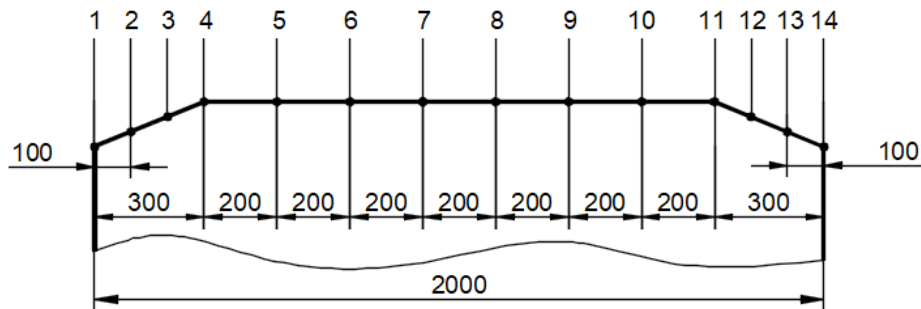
Точки измерения твердости поверхности бочки опорного вала
